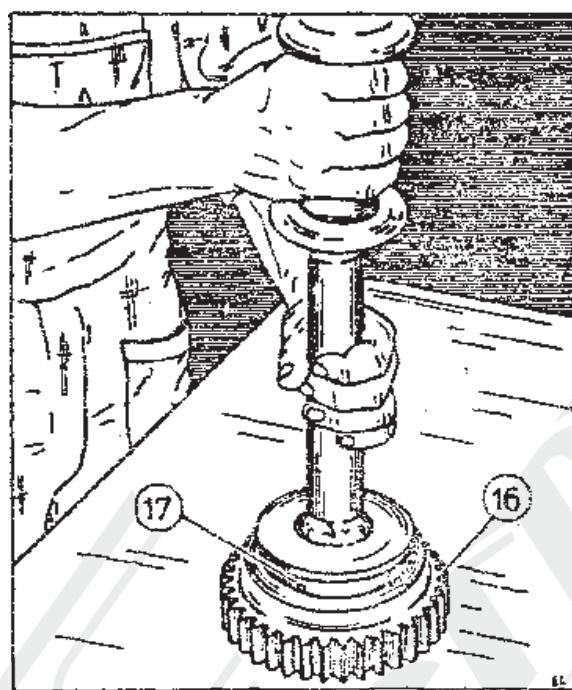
Вдавливание с помощью стержня шарикоподшипника 6014 /17/ в отверстие зубчатого колеса 16.
